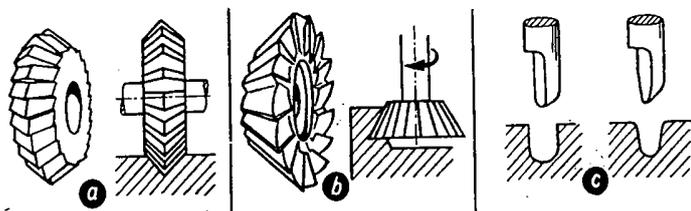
a), b) *Cylindrical milling cutters* dan c) *face end mill
